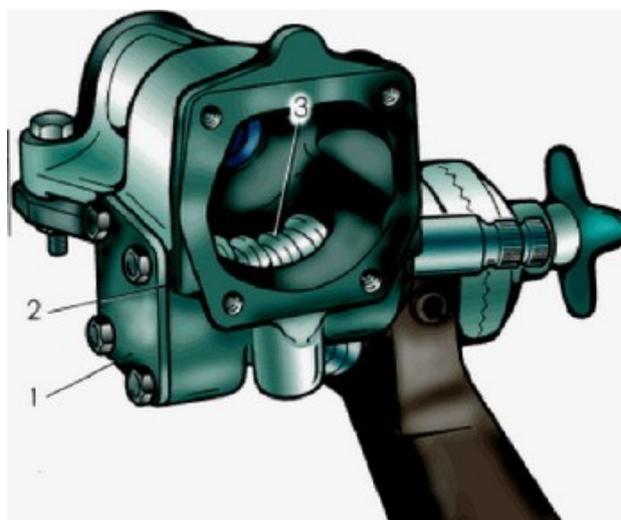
Снятие наружного кольца верхнего подшипника червяка: 1 - картер рулевого механизма; 2 - наружное кольцо верхнего подшипника червяка; 3 - оправка 67.7853.9541
